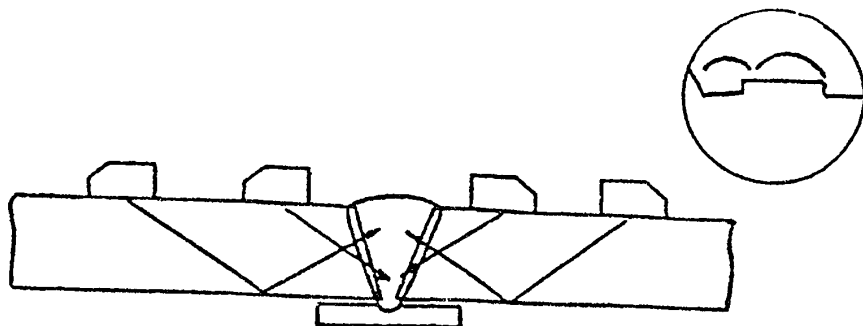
Схема контроля стыковых соединений с подкладными пластинами
